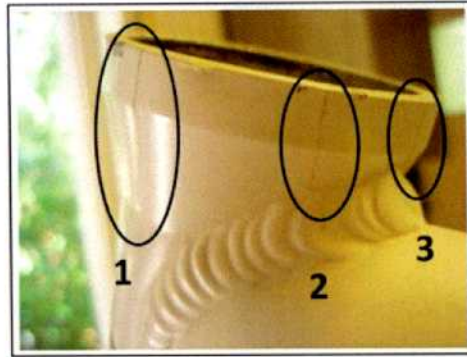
Cuadro 3, tubo de dirección fisurado.
